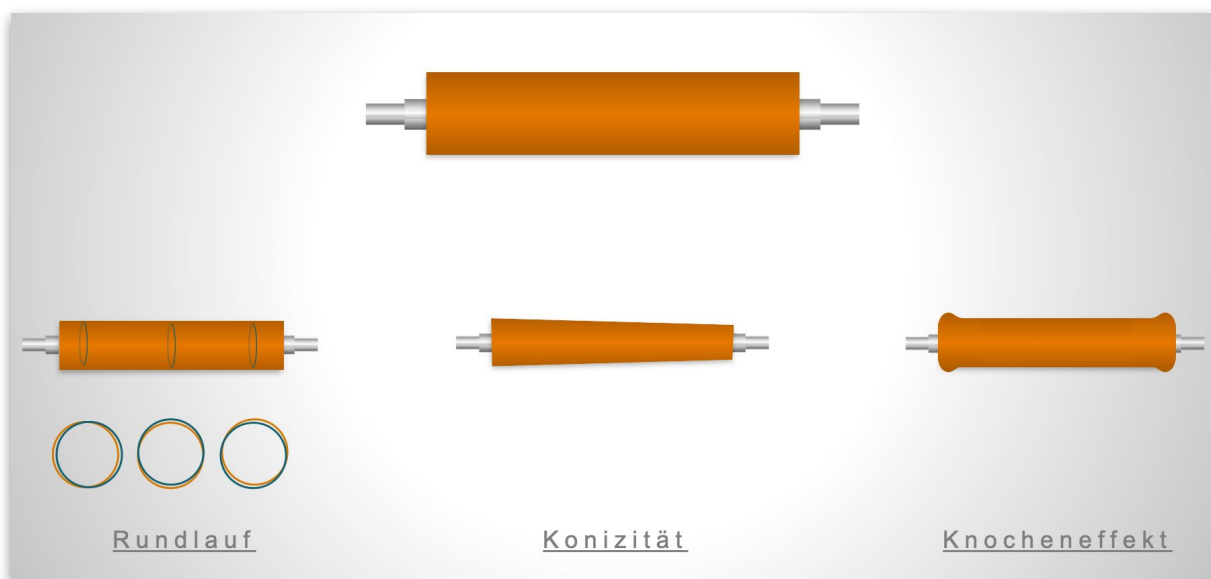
Fehler in der Zylindergeometrie führen zu Problemen im Druck
